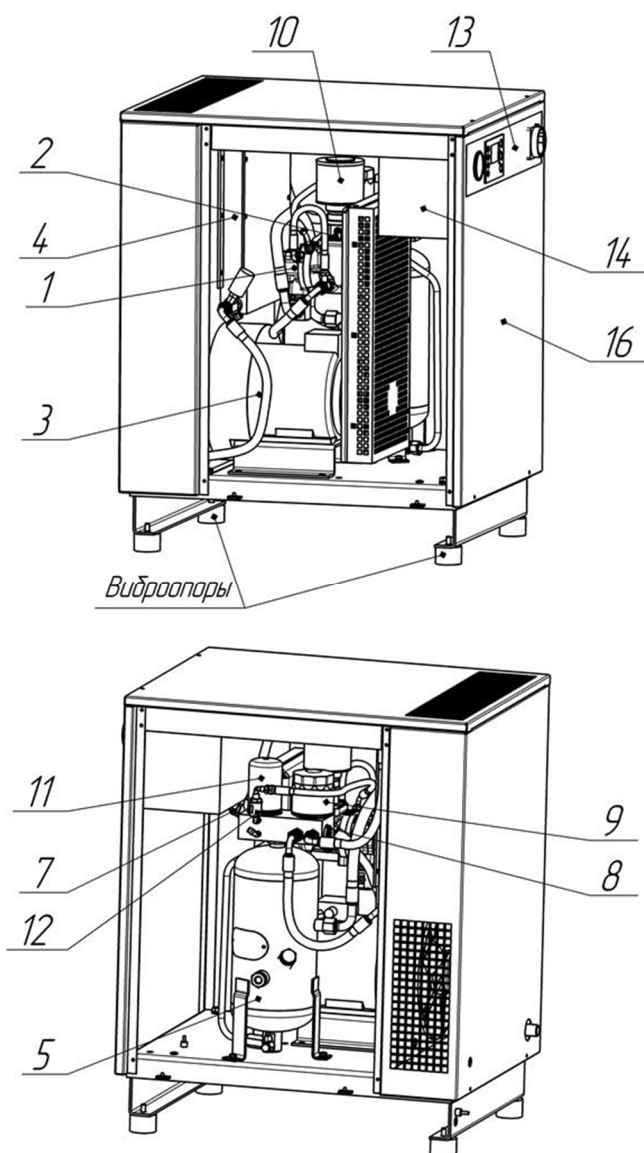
Общий вид компрессорной установки ВК5(7, 10)Е-...
